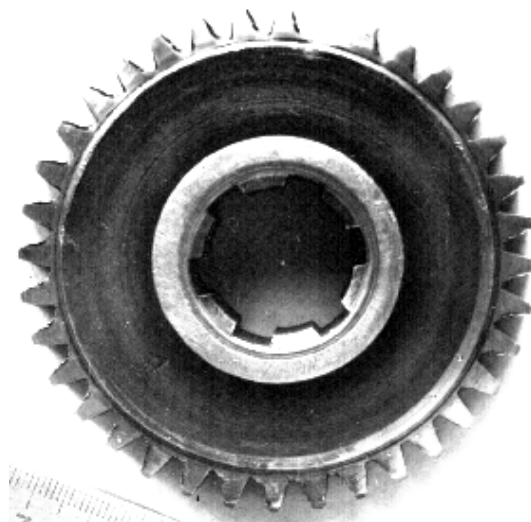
Поломка зуба шестерни токарного станка 1К62
